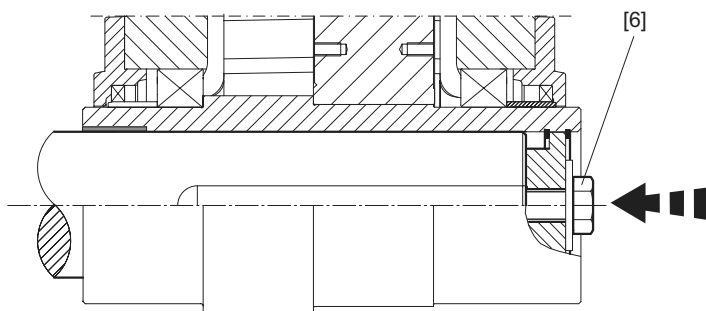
Reductor de eje hueco montado con unión por chaveta
